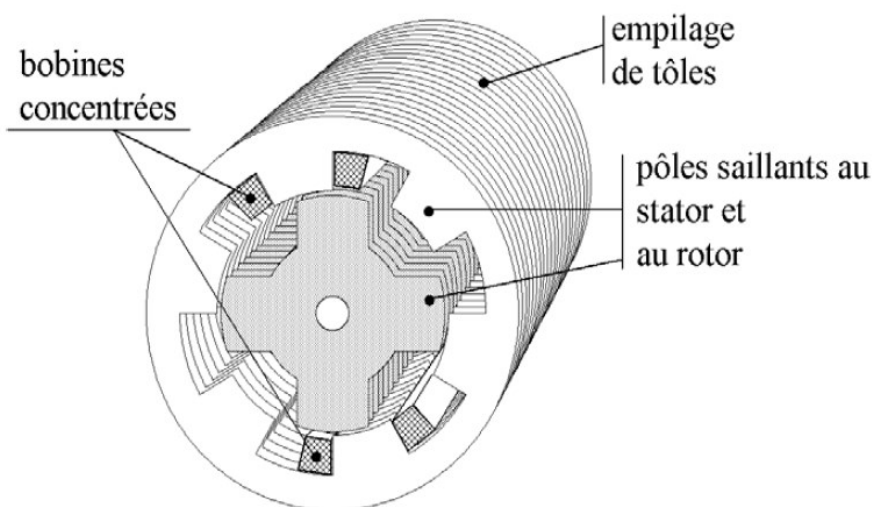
Assemblage du stator et du rotor de la MRVDS [3].
